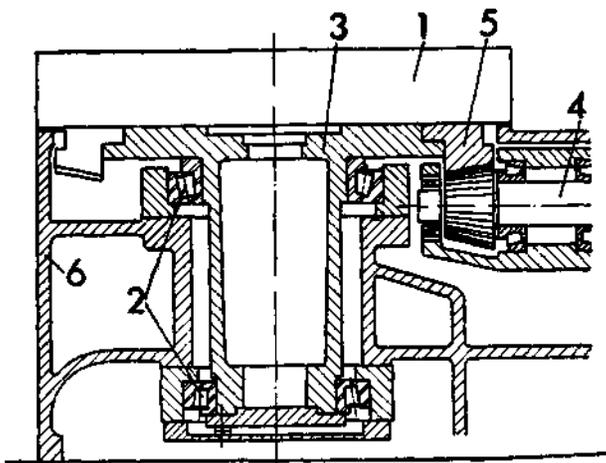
Esquema del montaje del eje principal sobre rodamientos: 1, plato; 2, rodamientos de guía y centraje; 3, eje principal; 4, piñón de ataque; 5, corona del plato; 6, banco.
